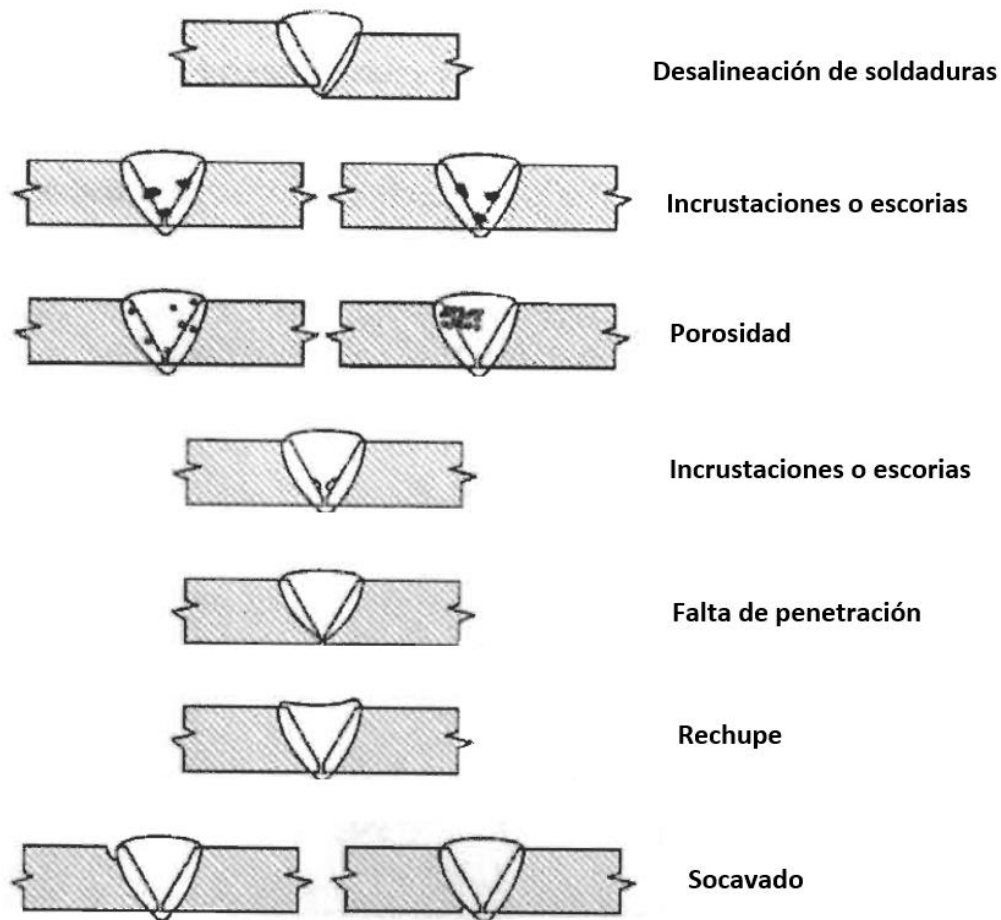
Defectos identificables en las soldaduras [14].
